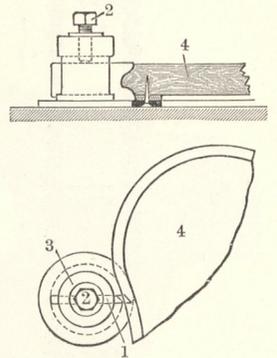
Fräser einer Holzfräsmaschine (Fräsen eines Profils nach Schablone).
